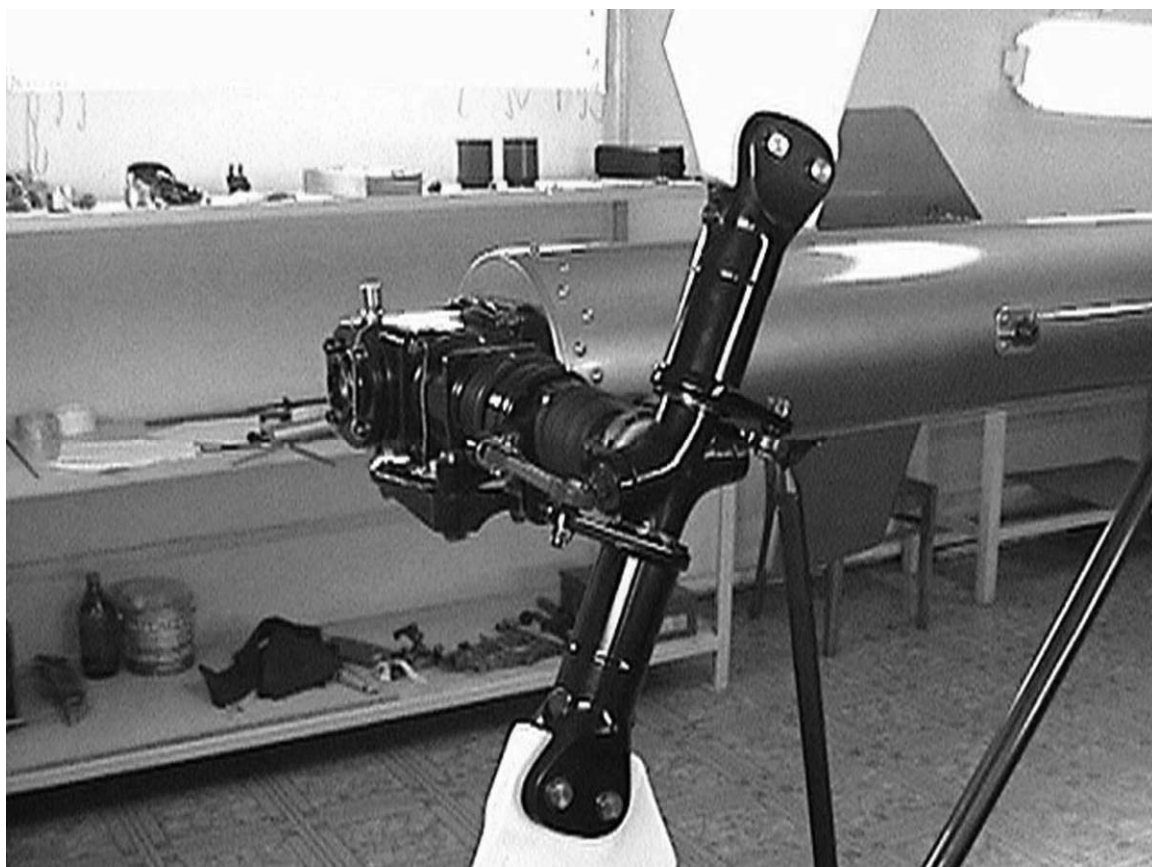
Хвостовой редуктор и втулка рулевого винта
